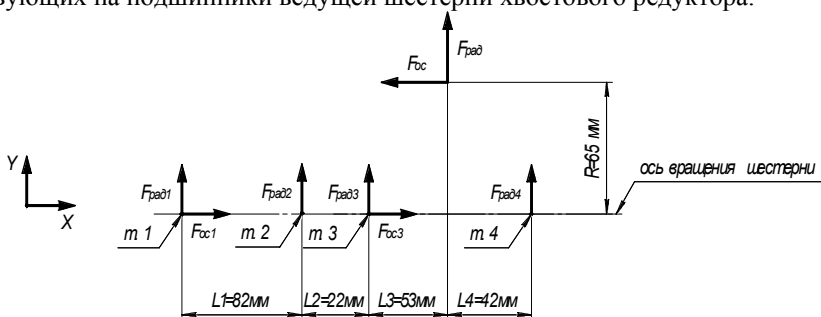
Расчетная схема для определения нагрузок, действующих на подшипники ведущей шестерни хвостового редуктора
